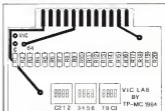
Assemblaggio dei componenti nel C5 VLJ
